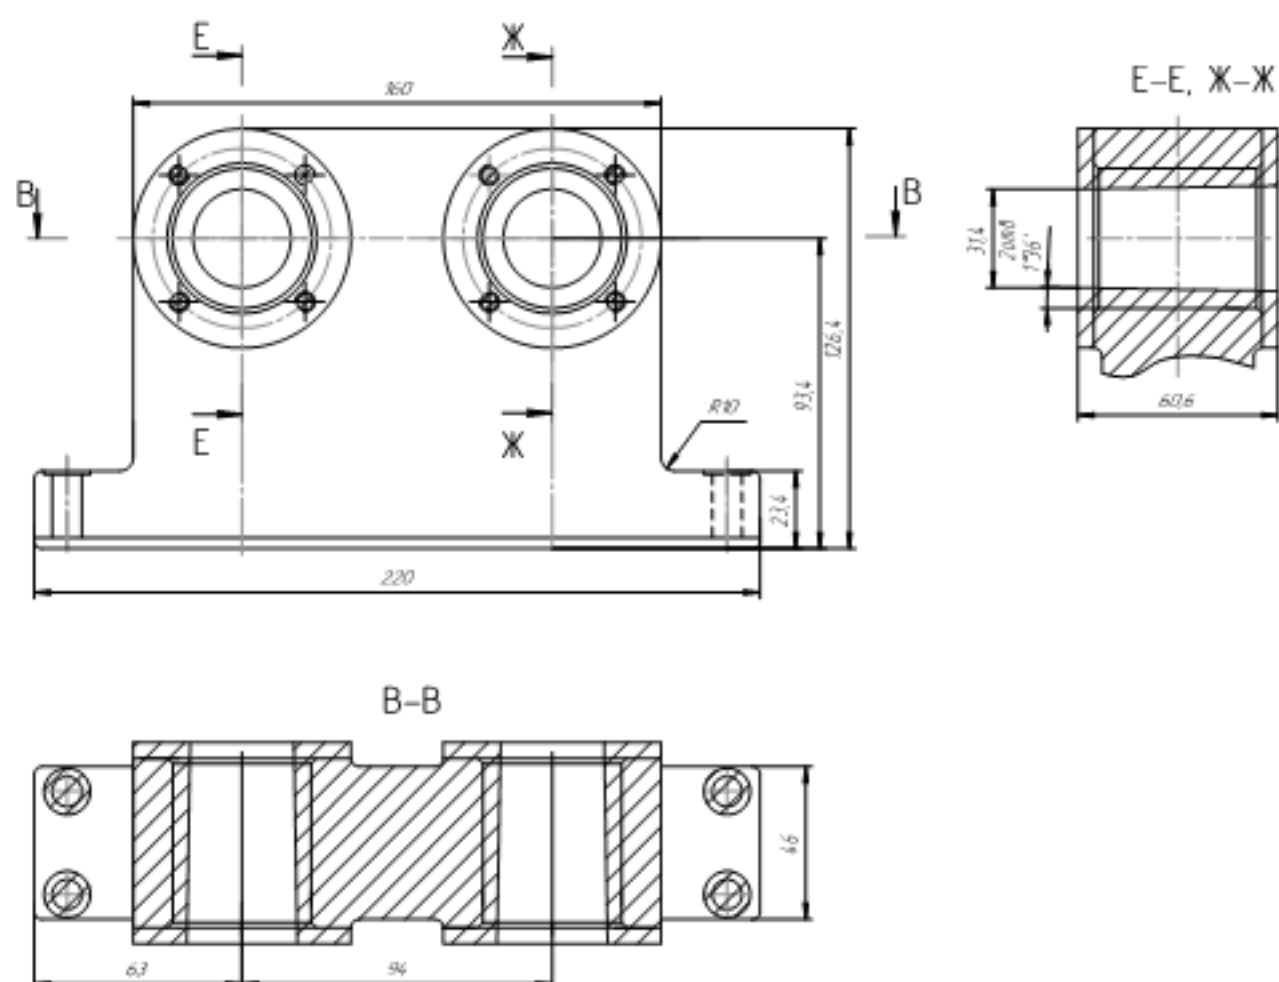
Заготовка виготовлена литтям в піщано-глинисті форми
